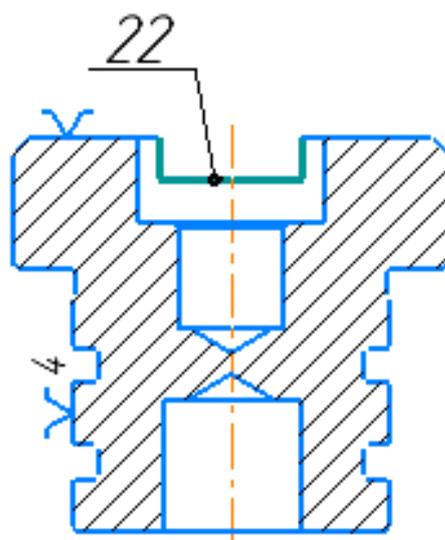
Эскиз вертикально-фрезерной операции
